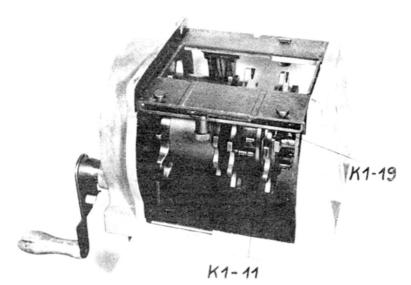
Gurtfüller 151; Gehäuse mit Getriebe, von rechts gesehen
